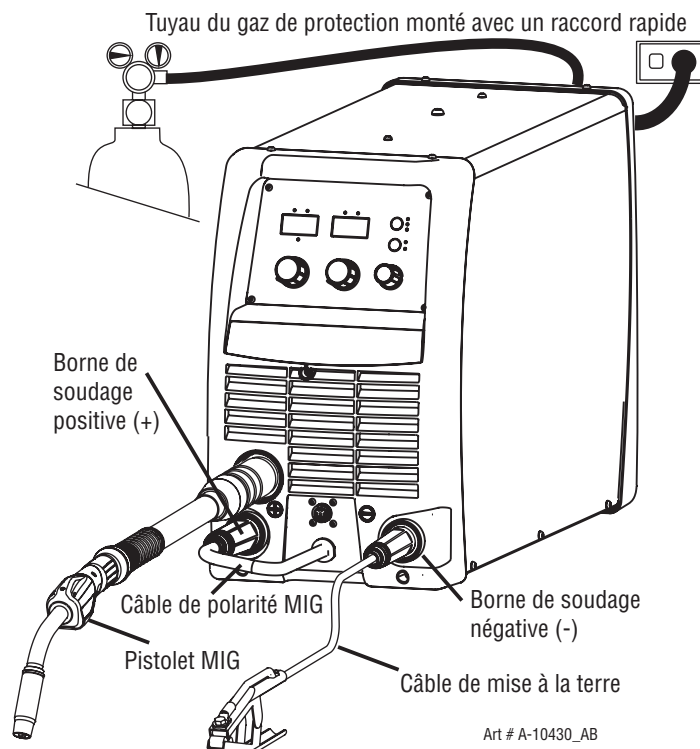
Configuration pour le soudage MIG avec le fil MIG protégé par gaz
